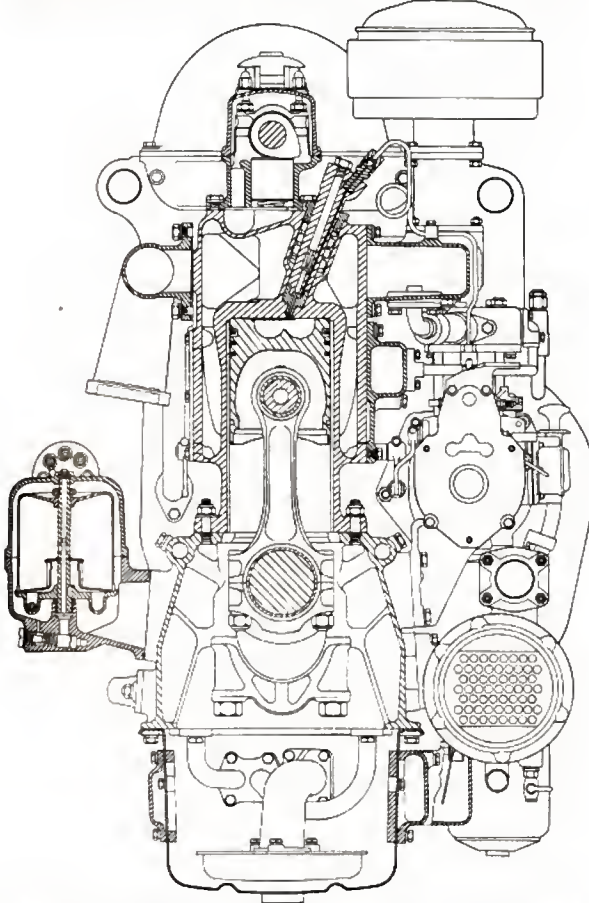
Coupe d'un moteur Diesel Leyland à cylindre borgne (Automobile Engineer)
